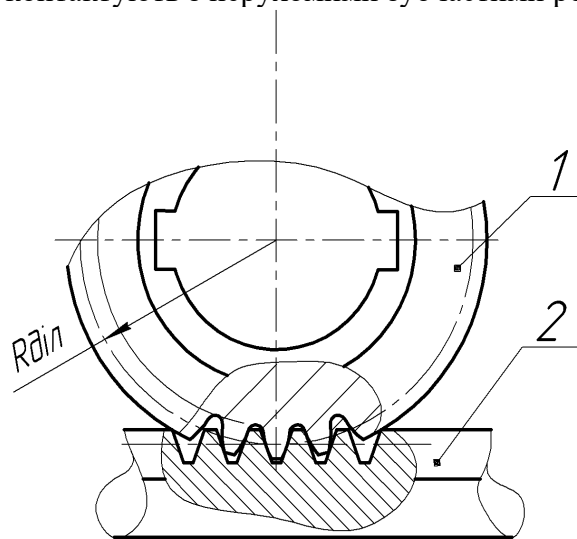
Ведуче зубчасте колесо та нерухома рейка станів холодної прокатки труб валками: 1 - валок; 2 – зубчата рейка; R_{dir} - дільний радіус ведучого зубчастого колеса
